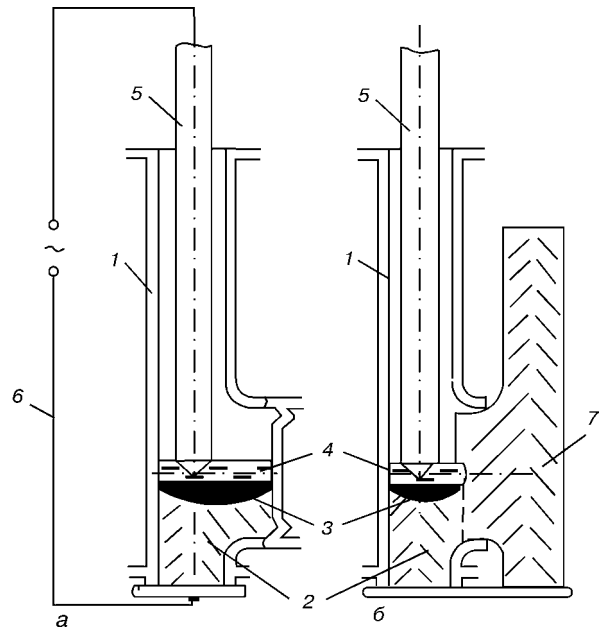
Схема изготовления кривошипа: а — выплавка первой щеки кривошипа с шейкой; б — выплавка второй щеки с приплавлением к шейке; 1 — кристаллизатор; 2 — выплавляемая заготовка; 3 — металлическая ванна; 4 — шлаковая ванна; 5 — расходный электрод; 6 — источник питания; 7 — приплавляемая часть
